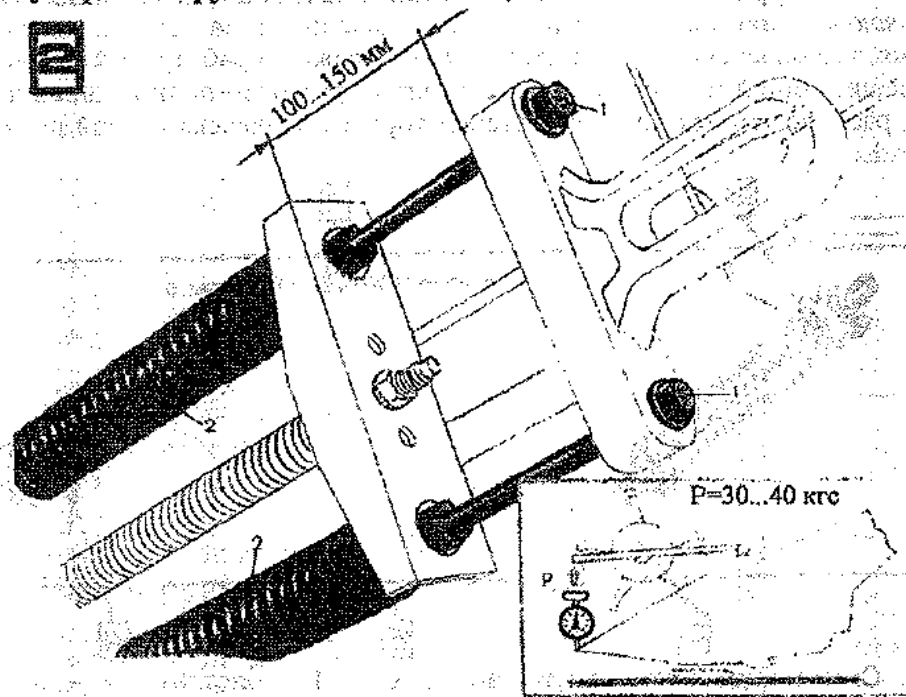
Схема пружинных блоков. 1 – болты регулировочные; 2 – пружинные блоки
